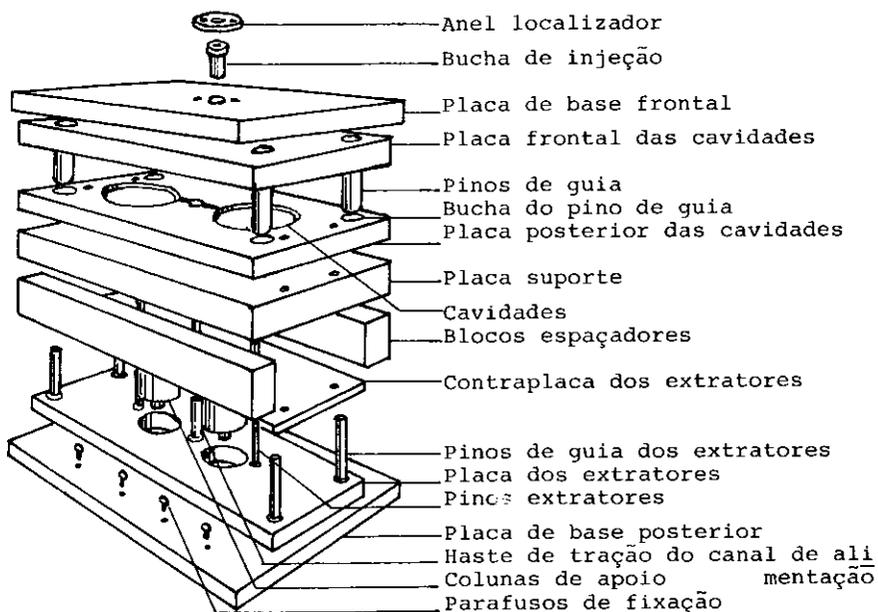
Vista explodida de um molde de injeção típico, de duas placas.
